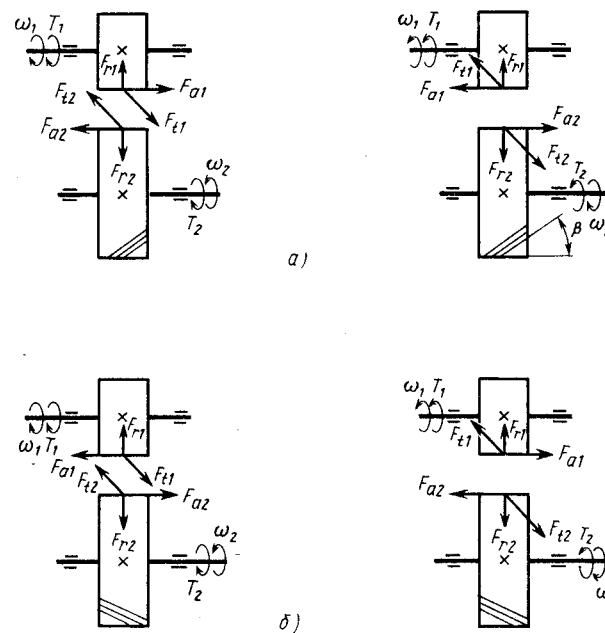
Схема сил в зацеплении косозубой цилиндрической передачи: а — направление линии зуба колеса — левое, шестерни — правое; б — колеса — правое, шестерни — левое
